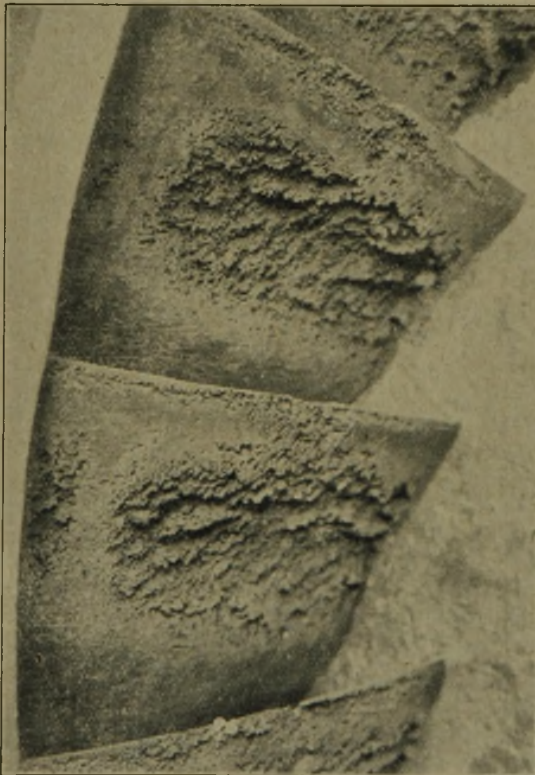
Anfrassung durch Hohlsoq am Laufradaustritt einer Wasserturbine.
